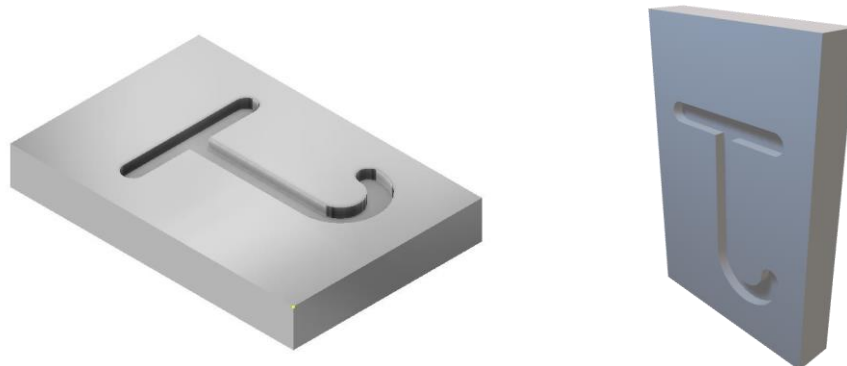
Τρισδιάστατη απεικόνιση αποστολής 11
